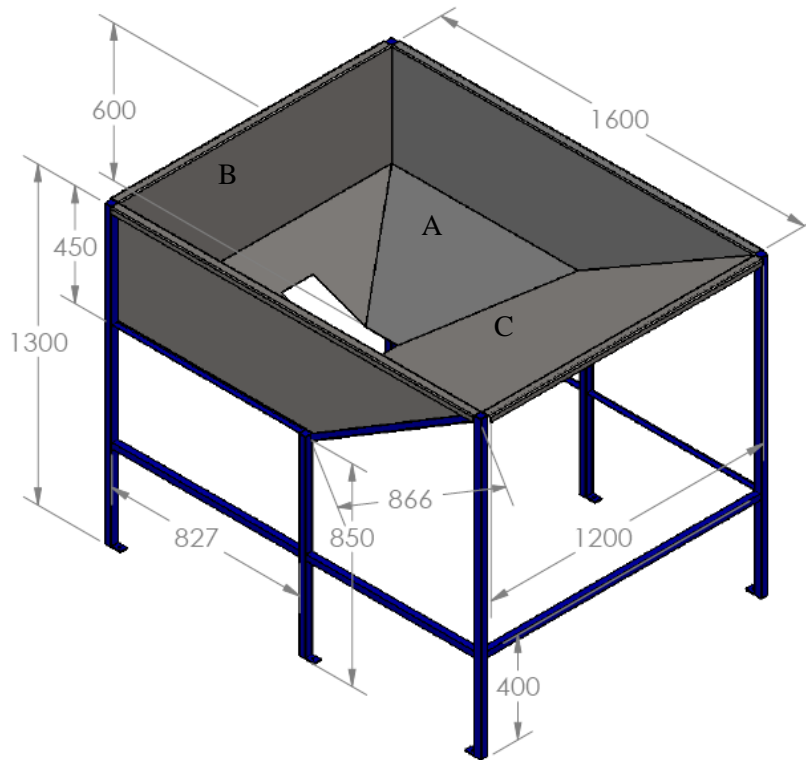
Dimensiones de la estructura de la tolva (mm)
